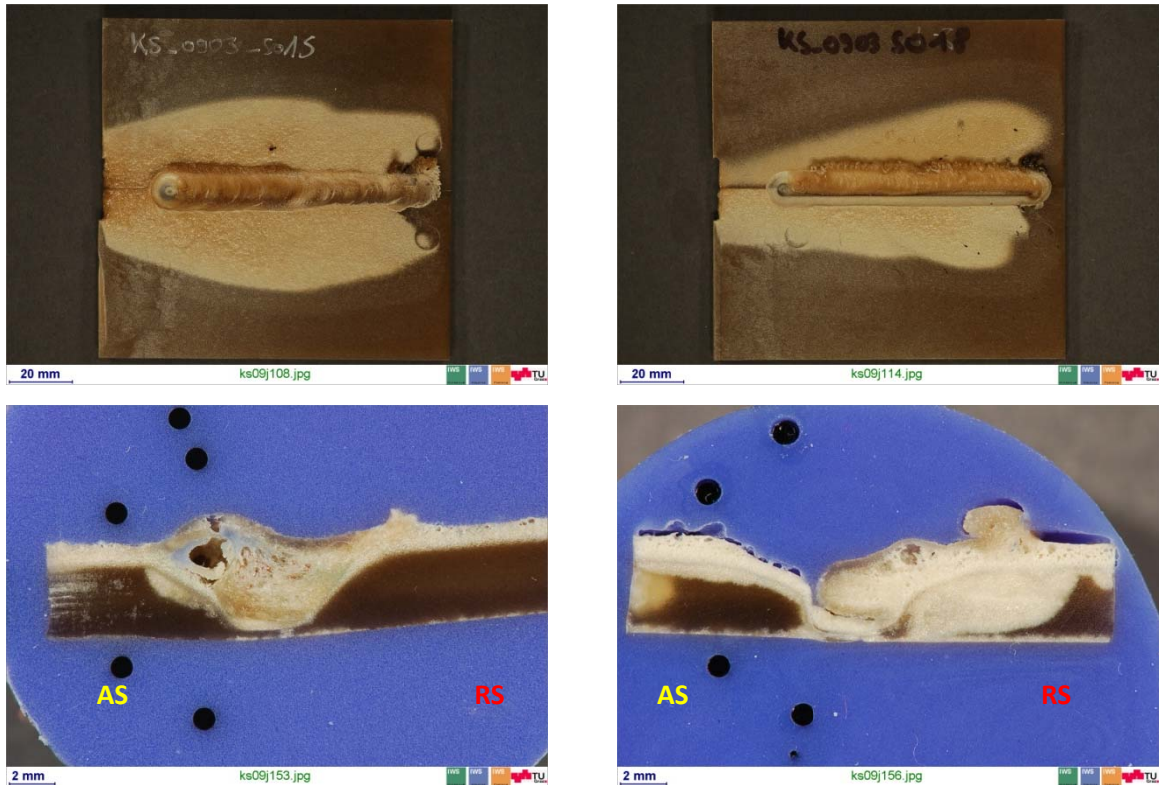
FSW von PES; Werkzeug 2 (links) und Werkzeug 3 (rechts)
